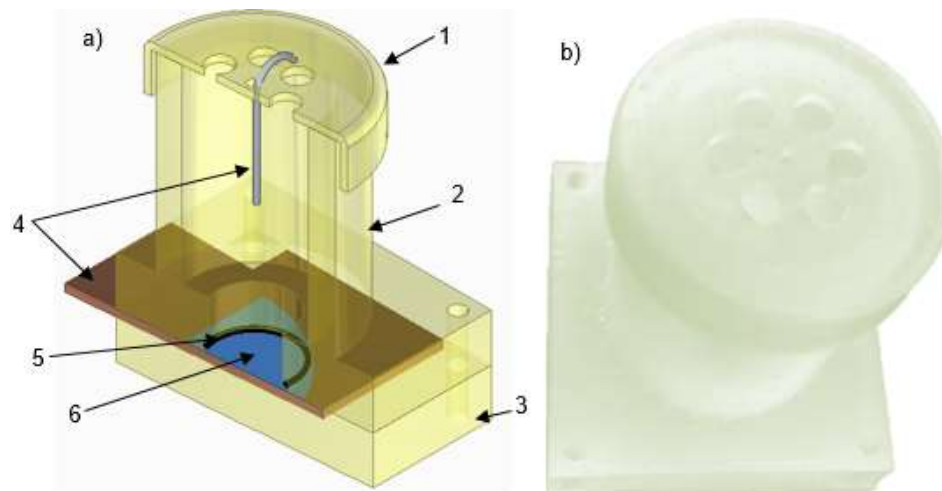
a) Partes del reactor diseñado en 3D mediante el software SolidEdge versión académica. b) Impresión 3D del reactor por SLA.
